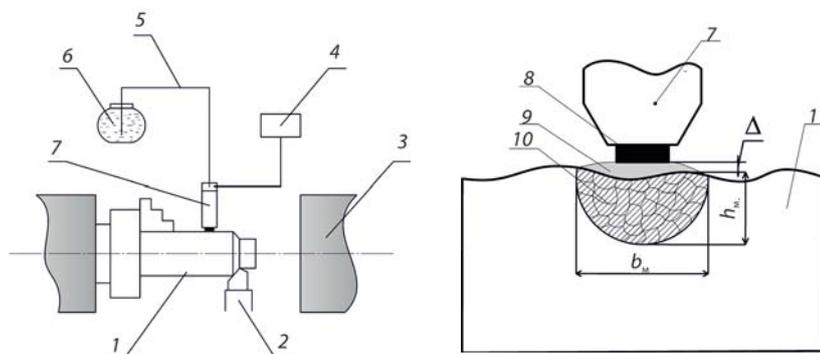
Схема нанесения локального криогенного воздействия при помощи устройства для подачи жидкого азота на обрабатываемую поверхность заготовки: 1 — заготовка; 2 — режущий инструмент; 3 — станок; 4 — баллон со сжатым воздухом; 5 — переливное устройство; 6 — сосуд Дьюара; 7 — устройство подачи жидкого азота; 8 — контактный элемент; 9 — жидкий азот; 10 — метастабильная структура
